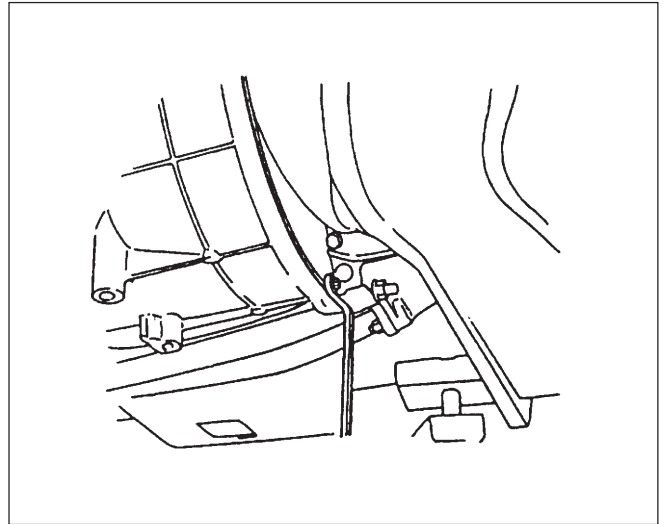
A - 11 Demontare platou inferior carcasă ambreiaj
